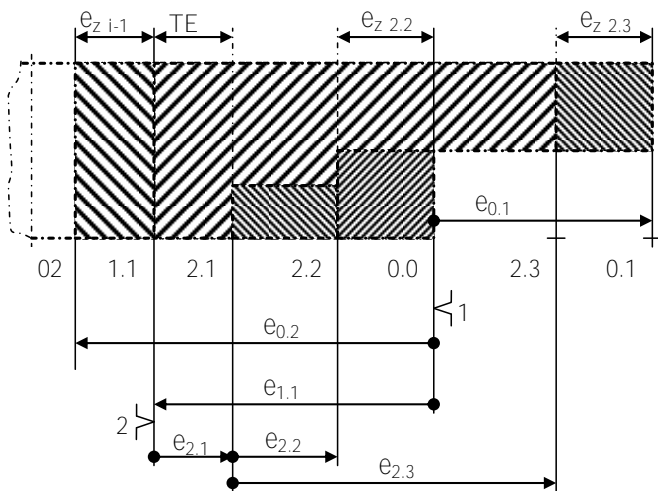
Схема обработки цилиндрических поверхностей с нанесенными эксцентриситетами
